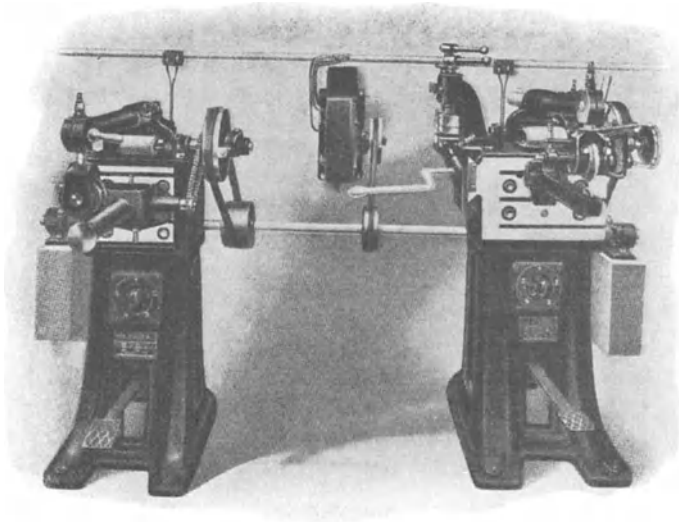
Längsnahtmaschine mit Motorantrieb und Stromunterbrechung.
